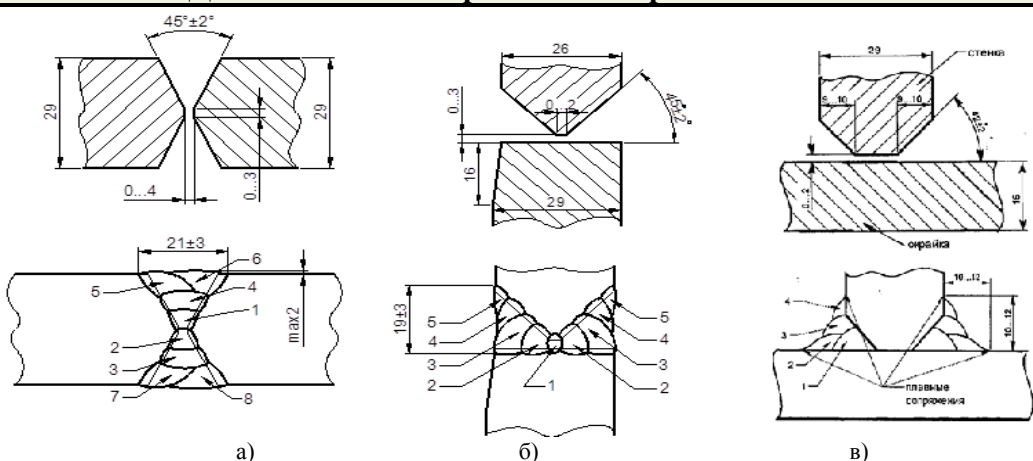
Схема ремонтного узла и порядок сварки
